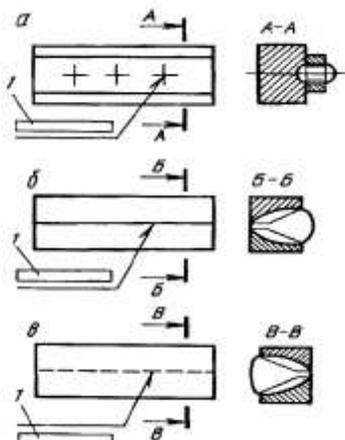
Условные изображения видимых и невидимых швов сварных соединений: а – видимый электрозаклепочный; б – видимый стыковой односторонний; в – невидимый стыковой односторонний; I – условное обозначение шва по ГОСТу
